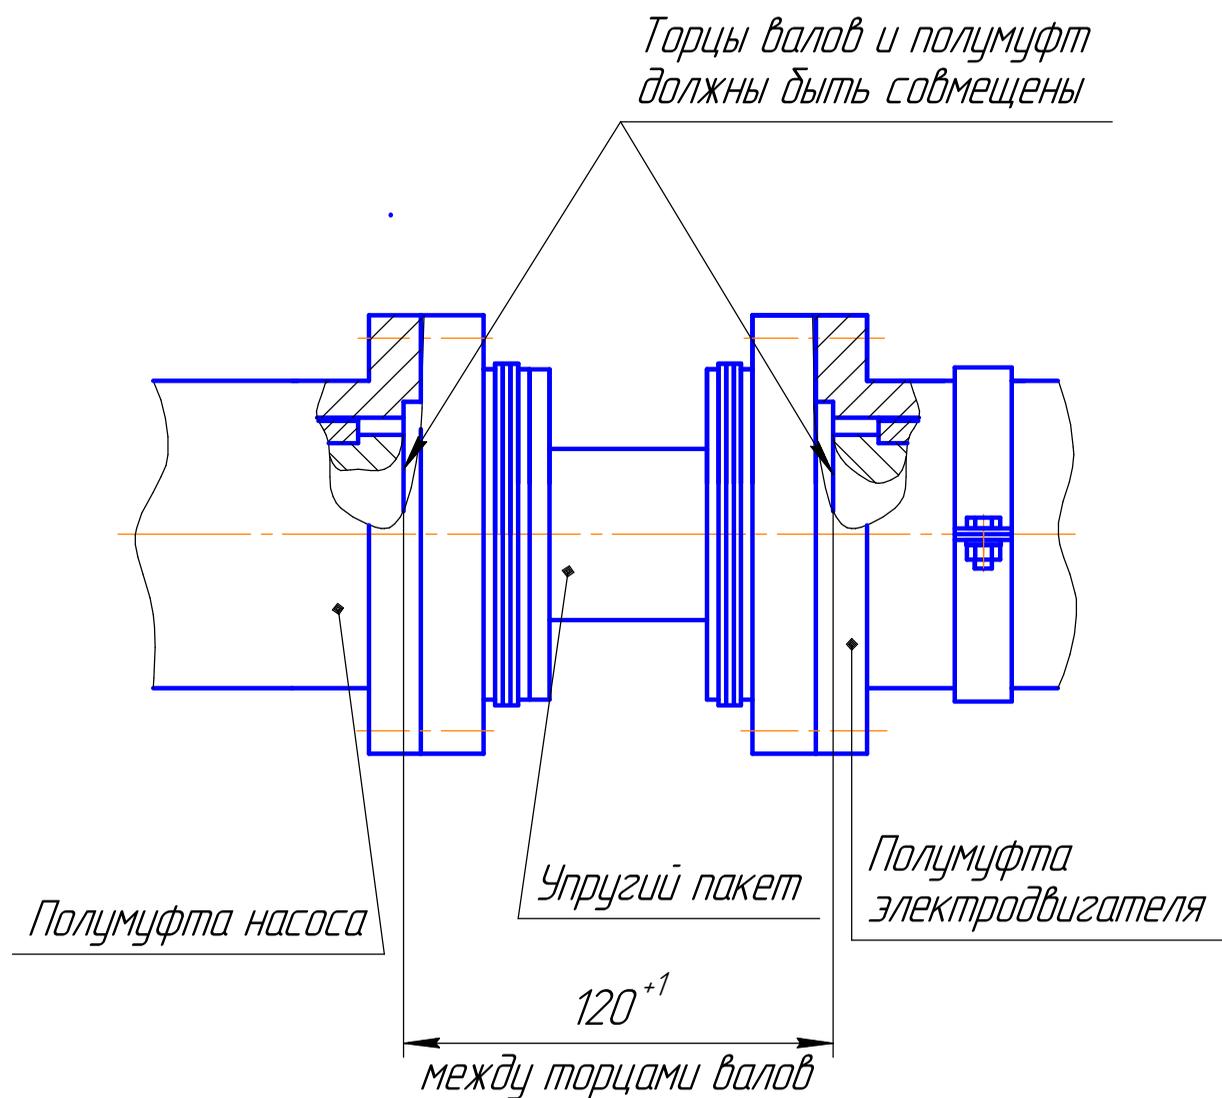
Устройство муфты МДП-2 и схема центровки валов
